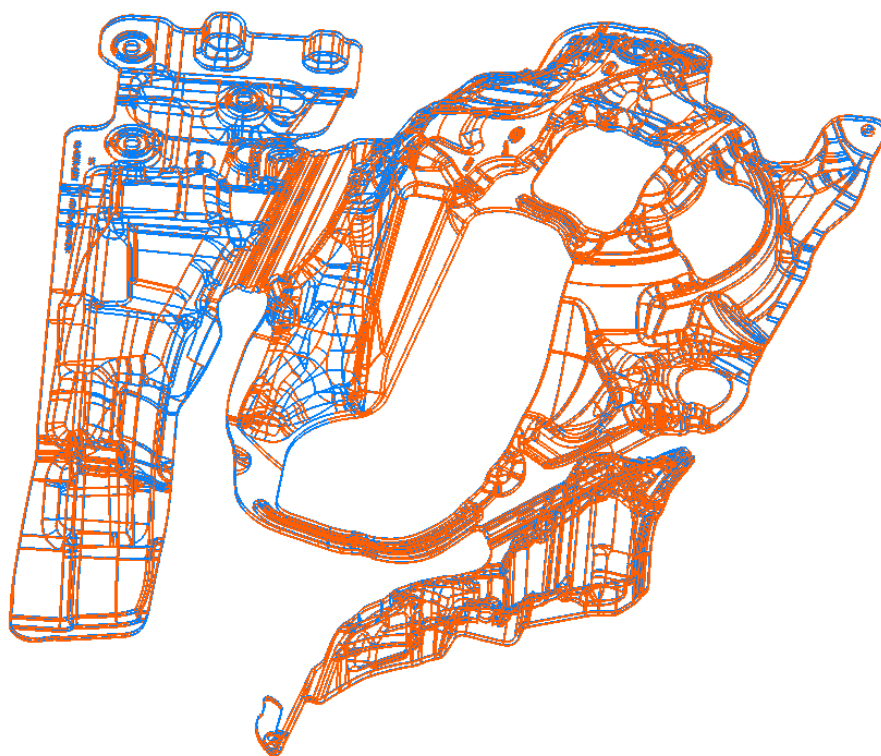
Obrázek horního bloku izometrický pohled ze zhora od základny [vlastní foto]
